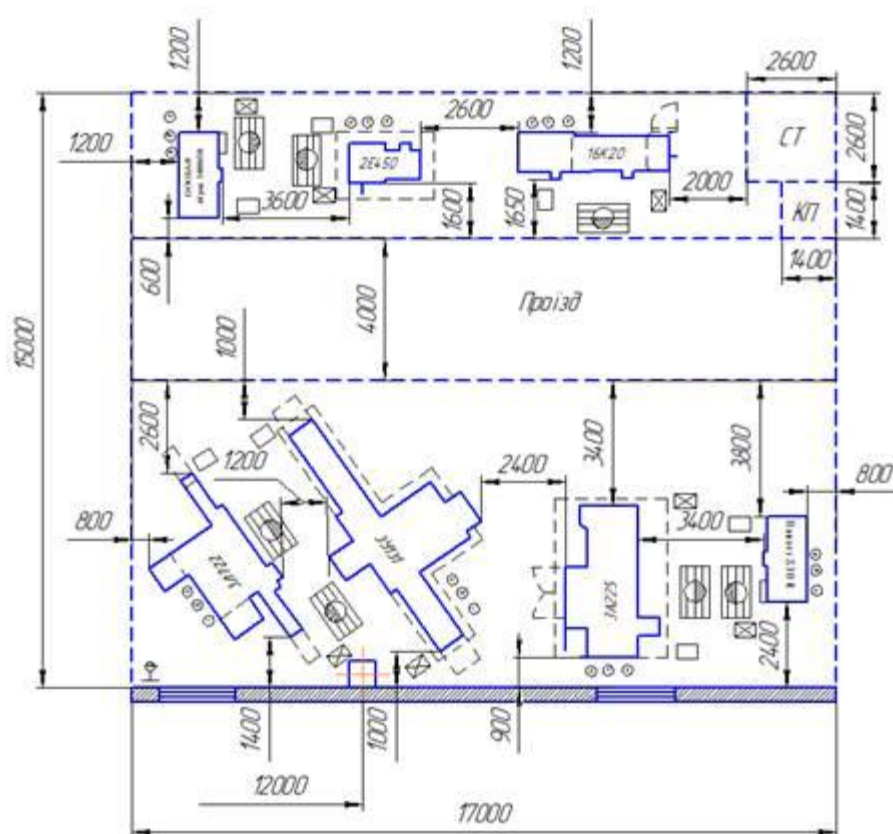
Конструктивна схема планування виробничого корпусу
